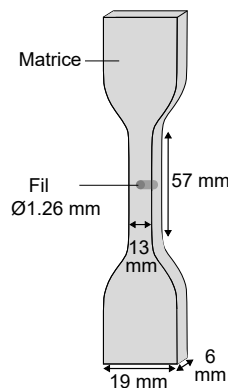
Géométrie et dimensions de l'éprouvette à matrice époxy.
